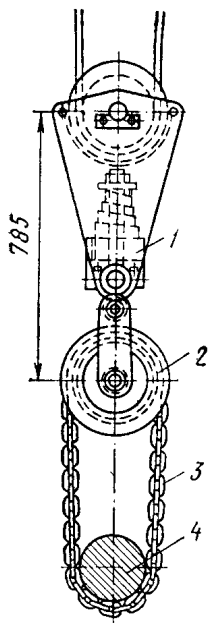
Устройство для ручного кантования с буферной подвеской:
